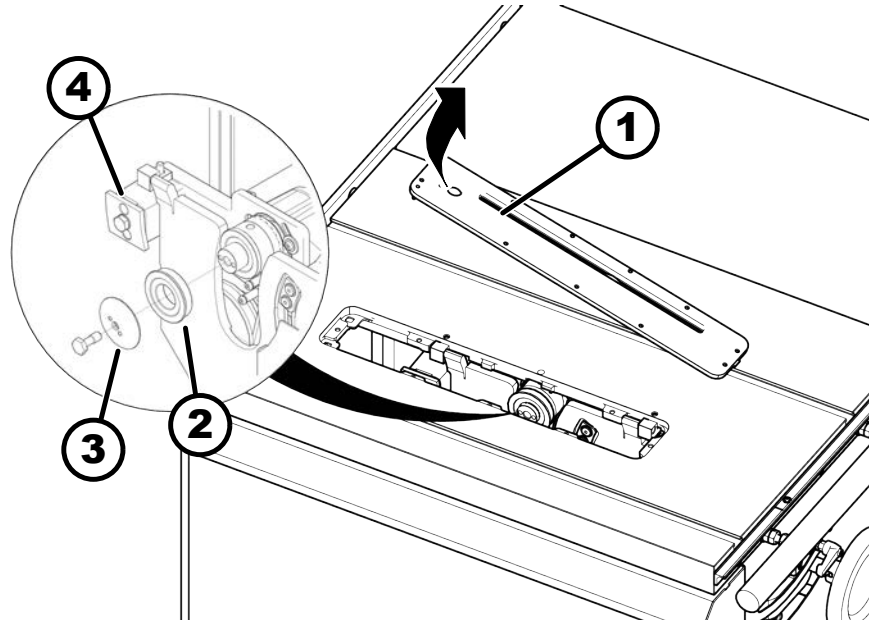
Hinterer Flansch / Spaltkeilhalter / Einlegebrett
